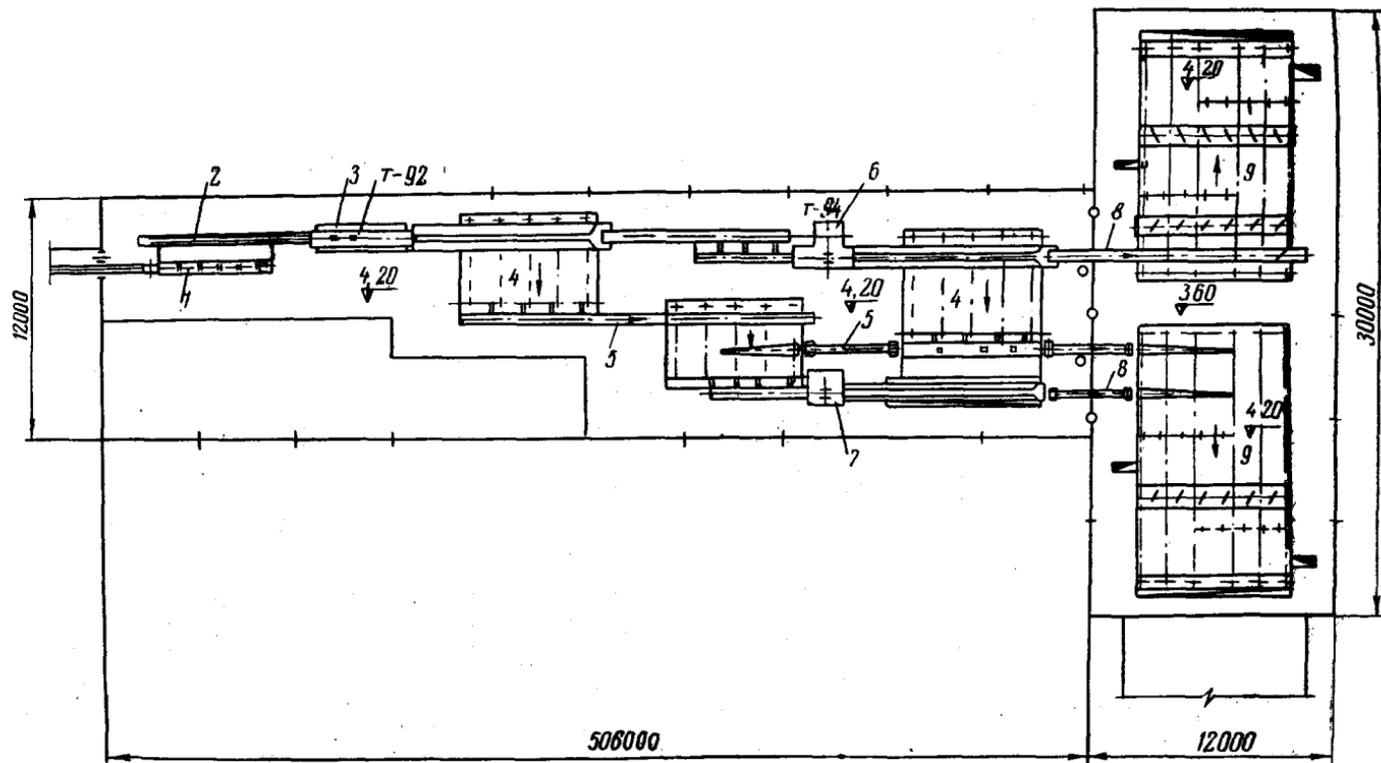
План лесопильного цеха, оборудованного двумя круглопильными станками, одним обрезным и двумя торцовочными агрегатами:
